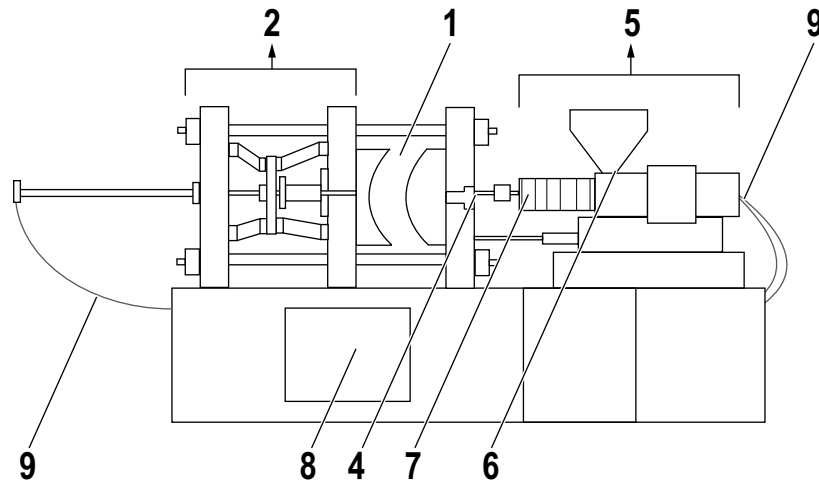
Zones de dangers pour la machine de moulage par injection (vue avant avec les protections retirées)
